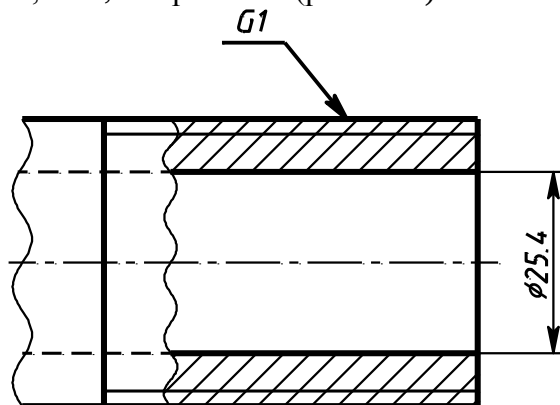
Обозначение трубной цилиндрической резьбы
